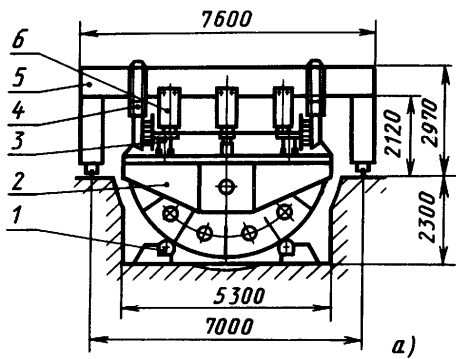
Основные этапы сборки и сварки двутавровых балок в полноповоротных кондукторах
